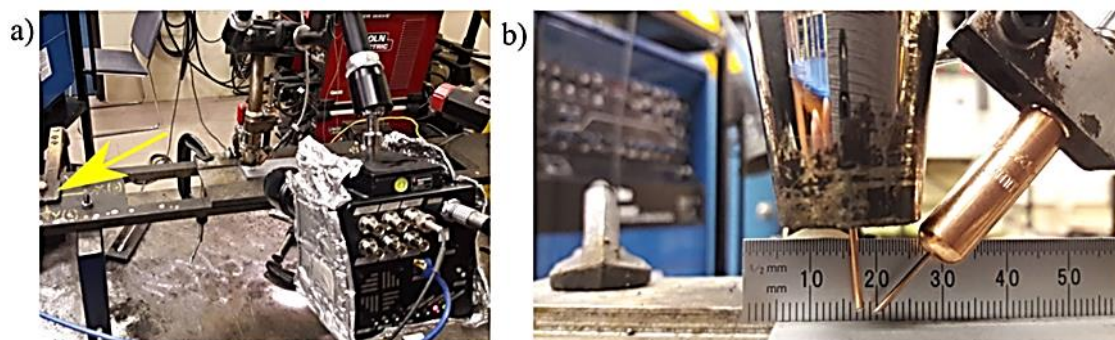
a) Configuração experimental usada para fabricar as soldas. (uma) Visão geral, da fonte soldagem, câmera e posto inicial de soldagem b) Detalhe do ângulo do arame frio.
